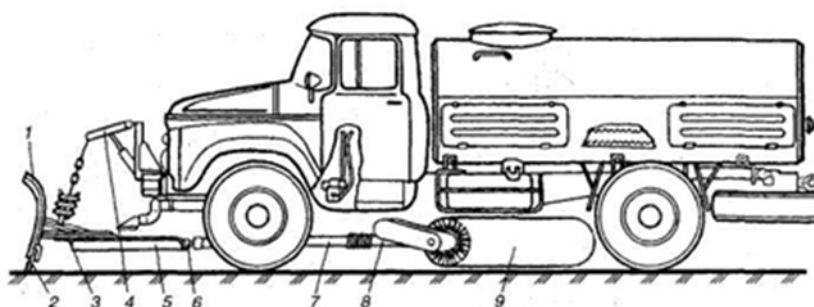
Плунжерно-щеточный снегоочиститель: 1 – отвал; 2 – секционный резиновый нож; 3 – поворотная рама; 4 – механизм подъема отвала; 5 – сцепная рама; 6 – вал; 7 – штанги; 8 – толкающая рама; 9 – цилиндрическая щетка
